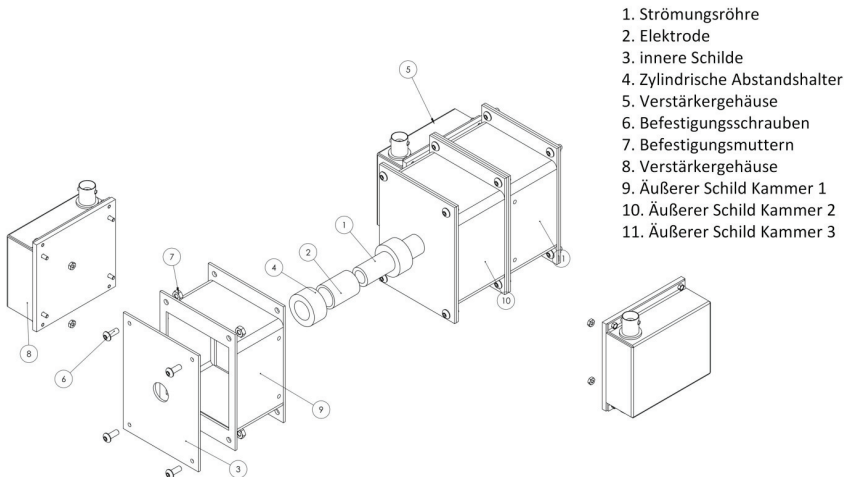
CAD Explosionszeichnung des Sensorkopfs [Bosch Bruguera, 2014].
